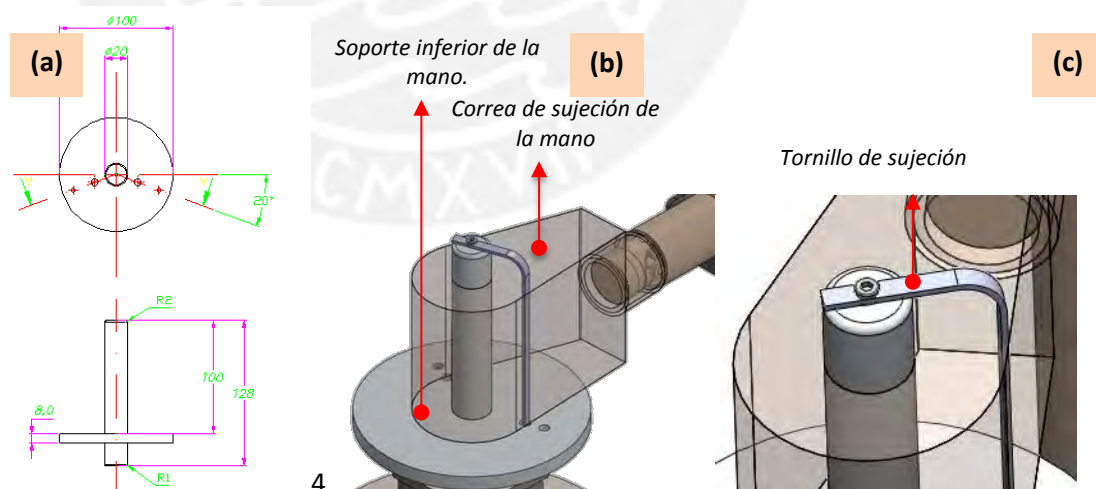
(a) Dimensiones generales del soporte de mano. (b) Posicionamiento de la mano indicando partes del soporte. (c) Tornillo de sujeción de la mano.
